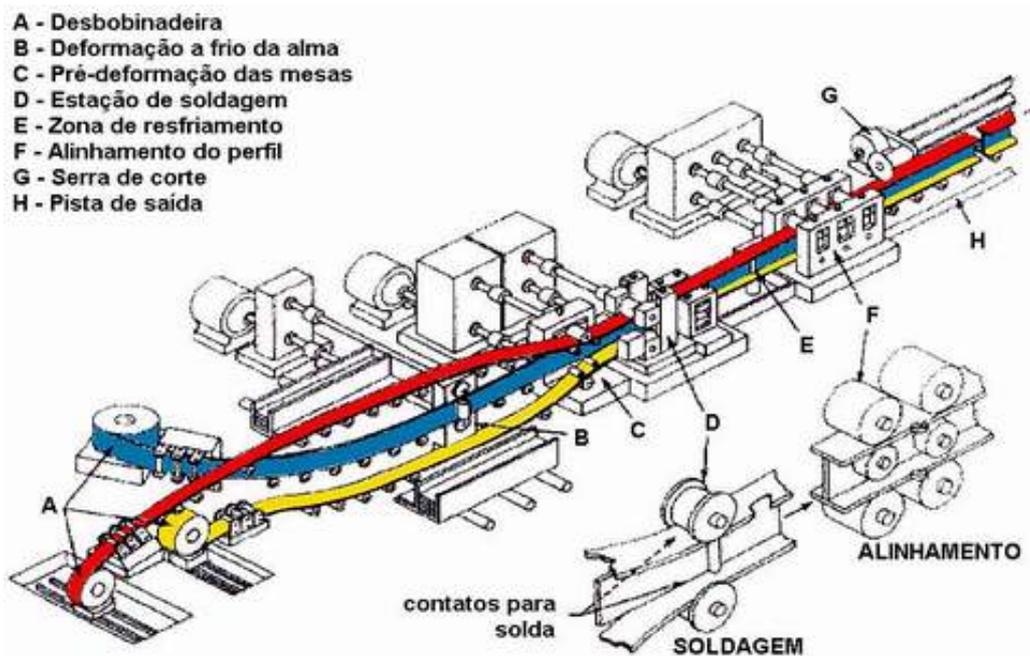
Esquema de produção dos perfis eletro-soldados da planta de Taubaté.
